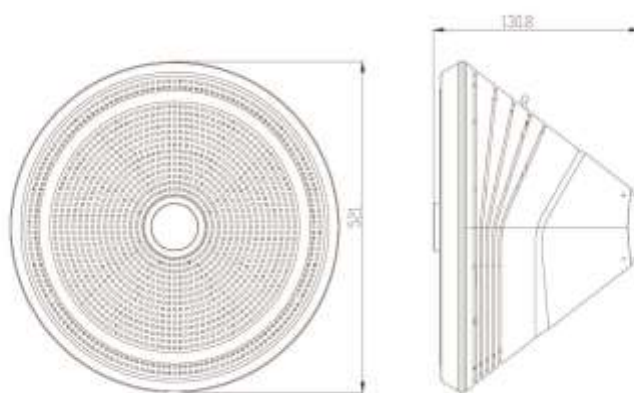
Dimensões principais do ventilador. Fonte: Autor.
